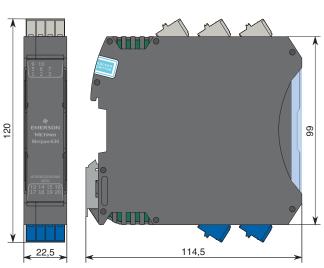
Габаритные размеры барьера в корпусе шириной 22,5 мм с разъемами с пружинными клеммниками и тестовыми гнездами
